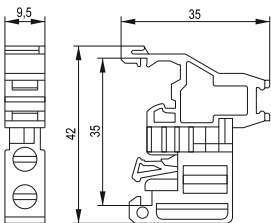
Габаритные и установочные размеры стопора концевого
